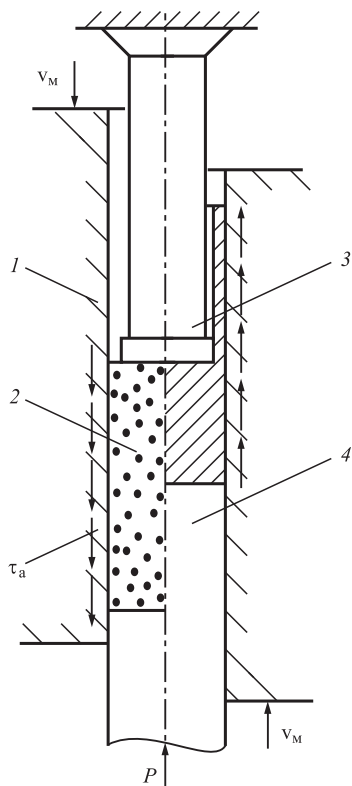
Устройство для удержания матрицы "на весу" при засыпке в нее порошковой шихты для двухстороннего формования заготовки
